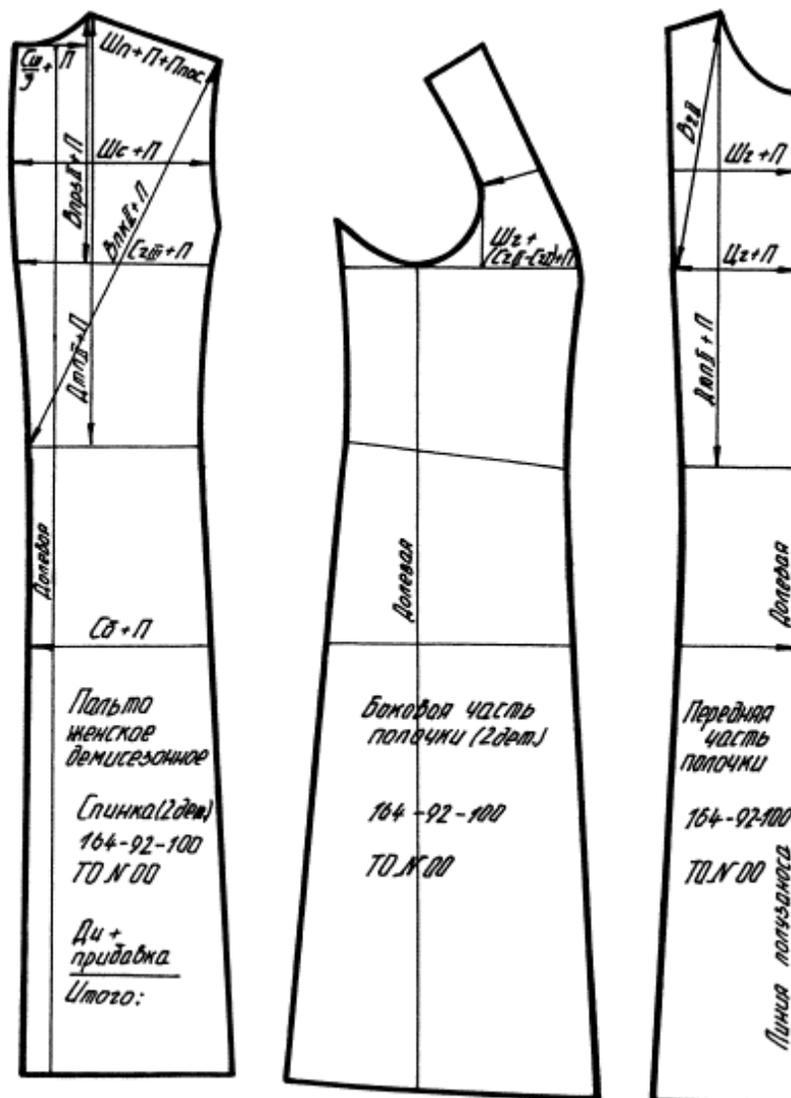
Рабочие чертежи лекал базовых конструкций
